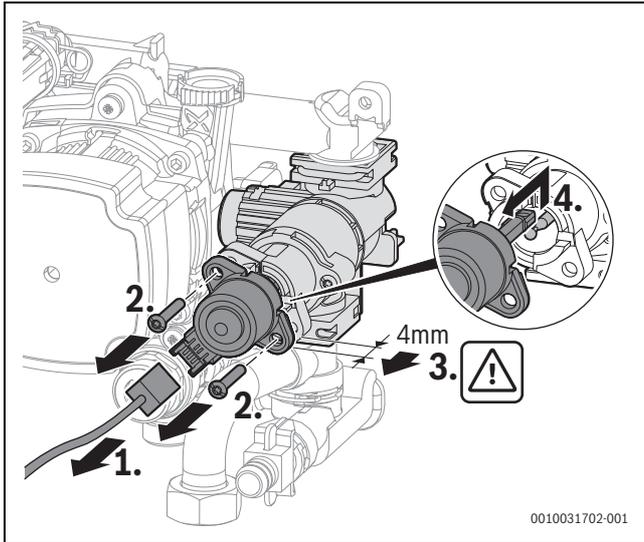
Motor am 3-Wege-Ventil ausbauen (Variante mit Schrauben)
